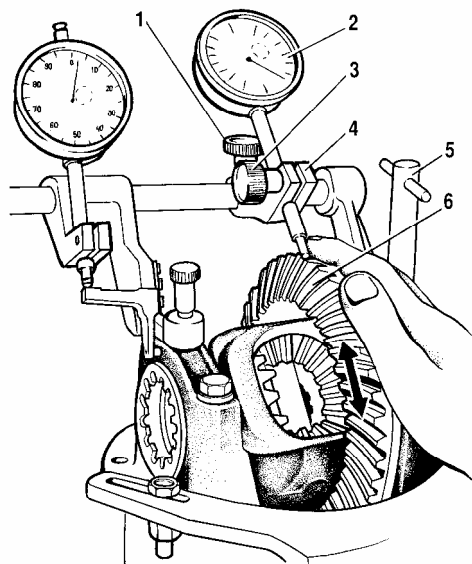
Проверка бокового зазора в зацеплении шестерен главной передачи приспособлением А.95688/R:
